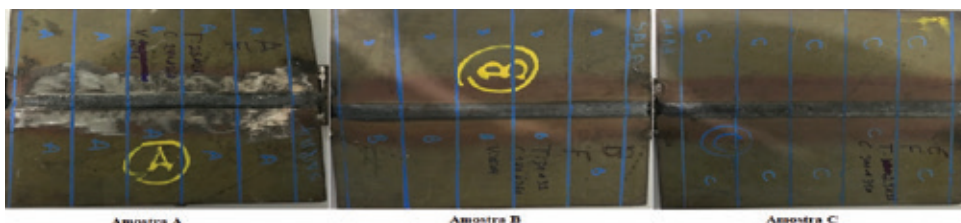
Junção de soldagem GMAW nas placas A – B – C.
